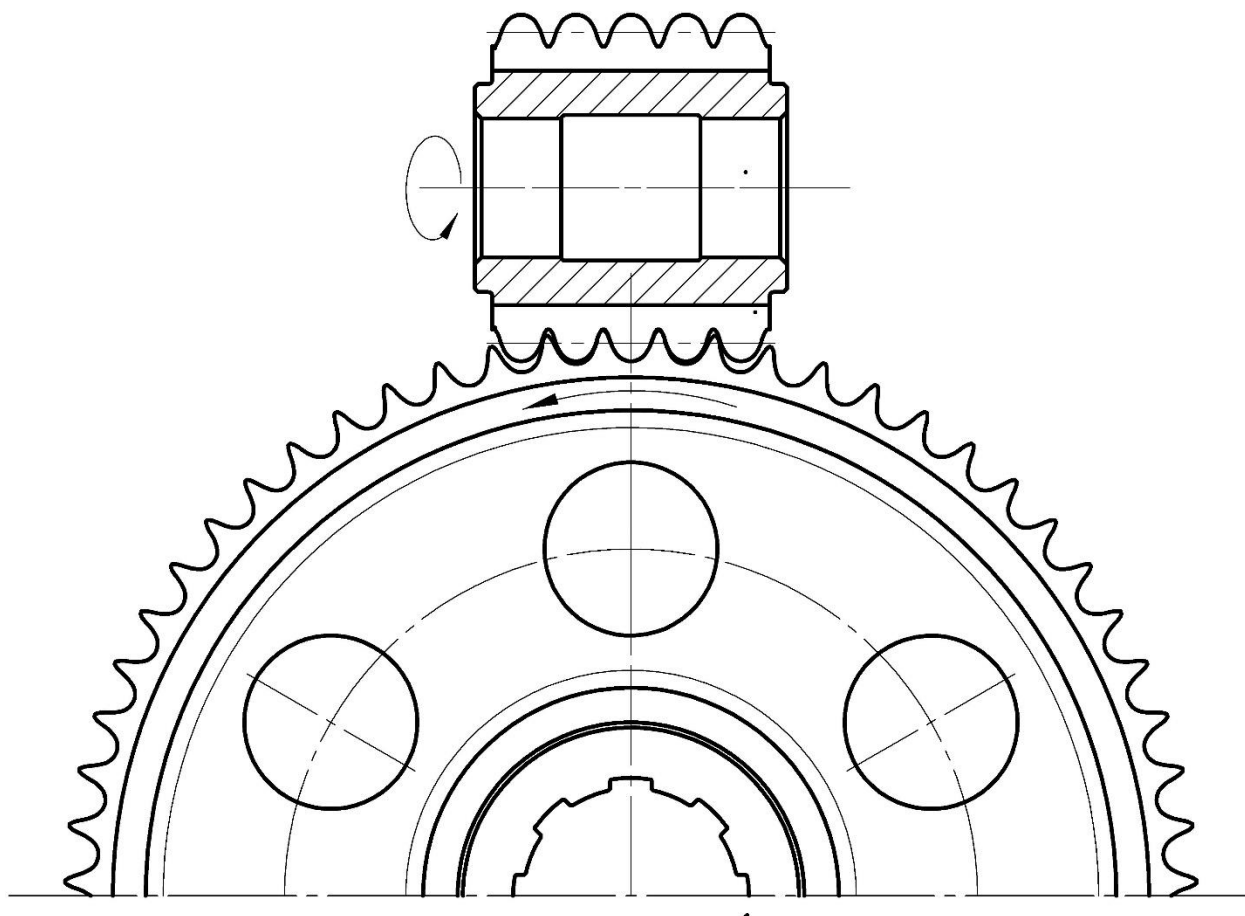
Нарізання зубів черв'ячною фрезою
